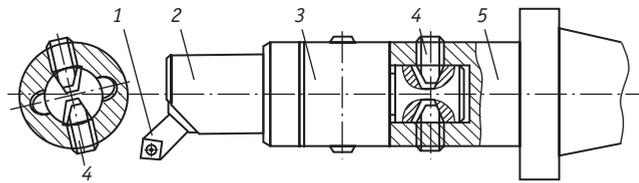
Модульный инструмент системы SKV: 1 – резец; 2 – удлинитель; 3 – переходник; 4 – винт; 5 – державка
